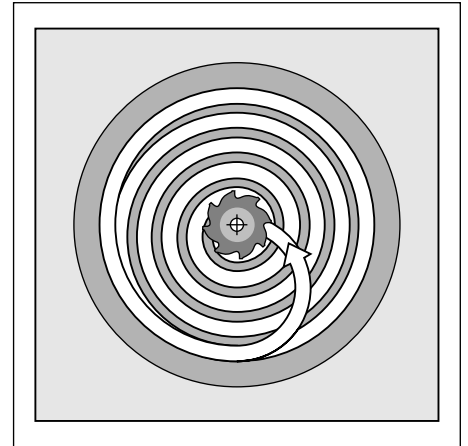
Werkzeug-Bahn beim Ausräumen
